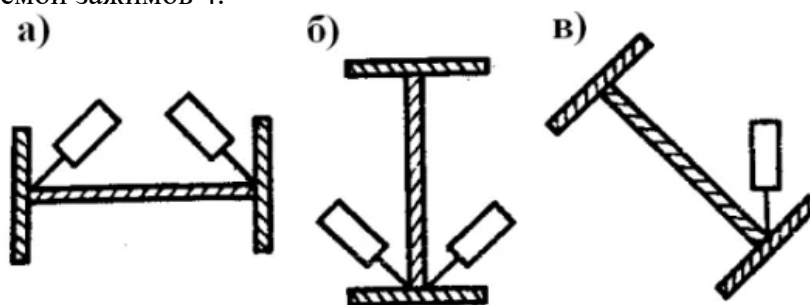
Способы укладки швов при сварке балок
